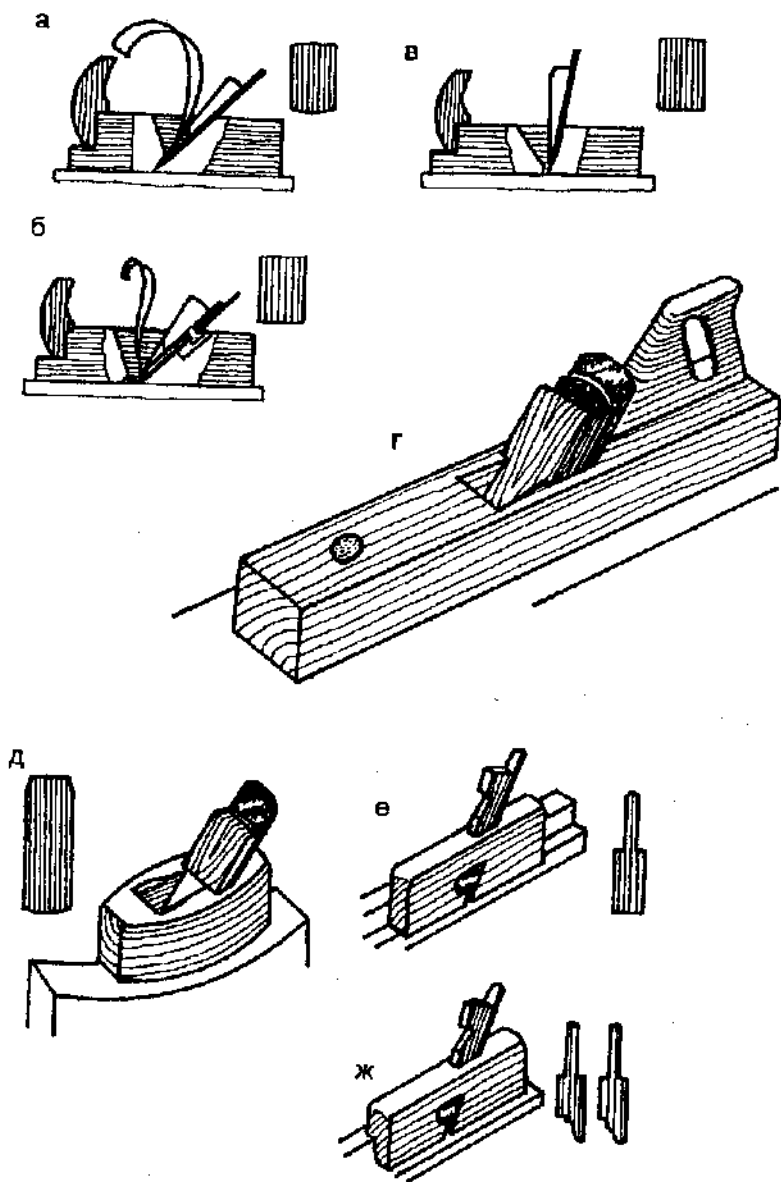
Строгальные инструменты: а — шерхебель; б — двойной рубанок; в — цинубель; г — фуганок; д — горбати́к; е — зензубель, ж — калевка
